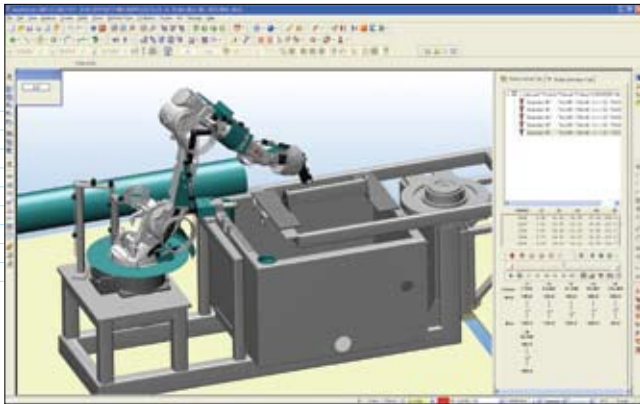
Сварочный робот, использующий наружную поворотную ось
